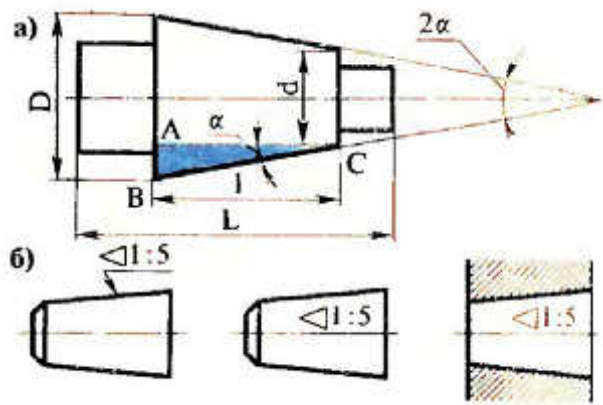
Элементы конической поверхности (а), условные обозначения конусности на чертежах (б)
